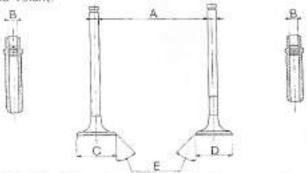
Dimensions principales des soupapes et des guides de soupapes
